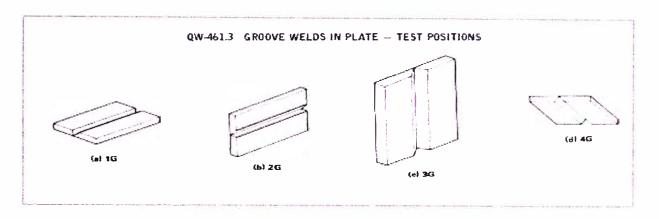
posiciones de prueba en planchas y Tubos – Juntas a Tope.
